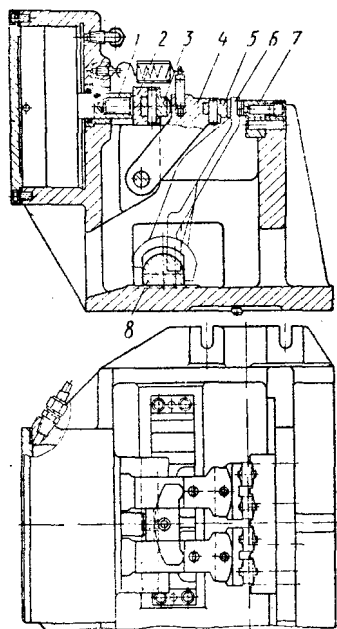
Приспособление для крепления четырех вилок при фрезеровании торцов
